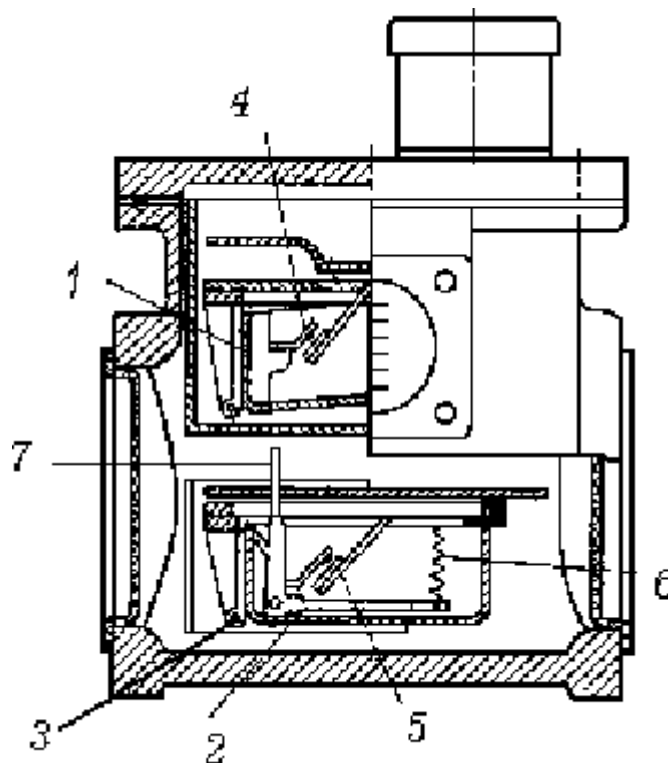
Конструкція газового реле чашкового типу
